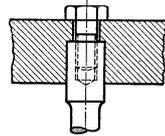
Stempelbefestigung durch Haftsitz und Zugschraube.
